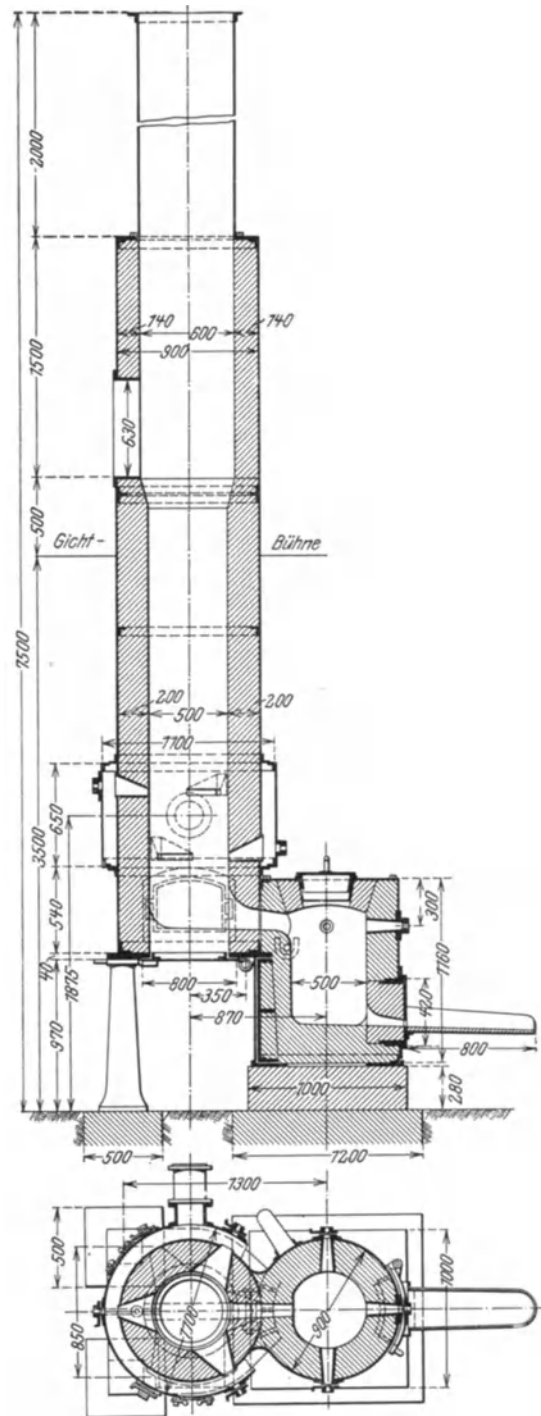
Älterer Kuppelofen der Badischen Maschinenfabrik.
